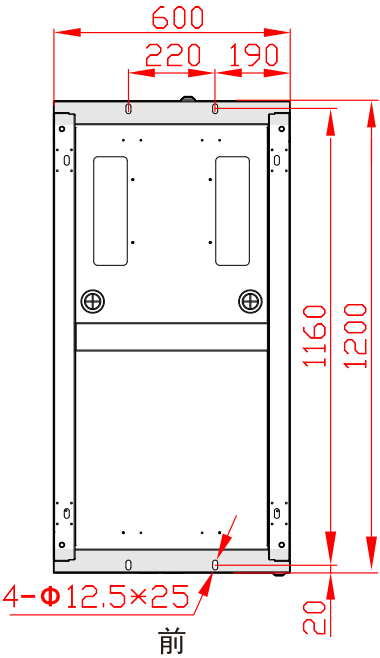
底座安装尺寸图 (仰视图, 单位: mm)
